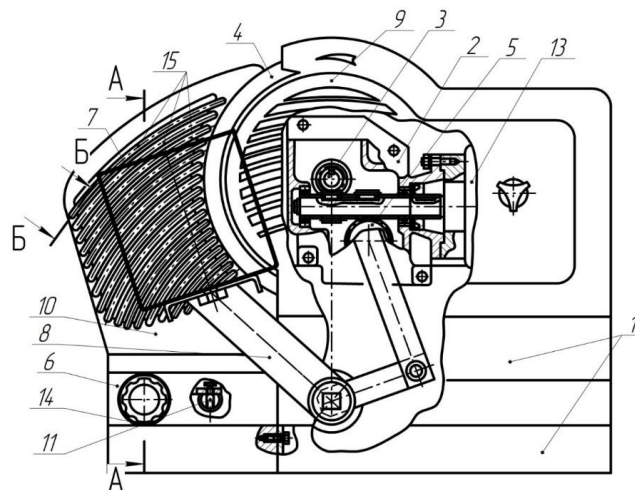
Машина для нарізання гастрономічних продуктів: 1 – корпус; 2 – черв'ячний редуктор, 3 – приводний вал дискового ножа, 4 – дисковий ніж, 5 – приводний вал кривошипно-коромислового механізму; 6 – механізм регулювання товщини; 7 – завантажувальний лоток; 8 – важіль подачі продукту; 9 – щиток; 10 – опорний стіл; 11 –направляюча, 13 – електродвигун, 14 – ручка, 15 – прутки столу.
